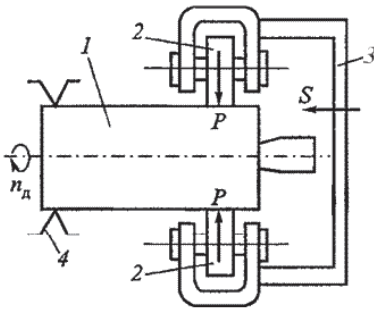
Схема обкатування: 1 — деталь; 2 — накатний ролик; 3 — роликовий обкатник; 4 — патрон токарного верстата; P — сила тиску на ролик; S — подача ролика в осьовому напрямку; n_d — частота обертів деталі
